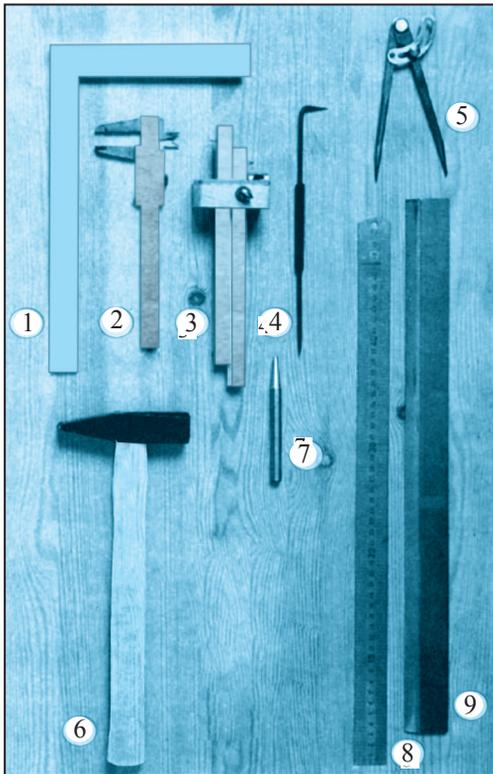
Измерительные и разметочные инструменты: 1 – 90°-ный угольник; 2 – штангенциркуль; 3 – масштабная линейка; 4 – металлическая чертилка; 5 – разметочный циркуль; 6 – слесарный молоток; 7 – кернер; 8,9 – линейки.
